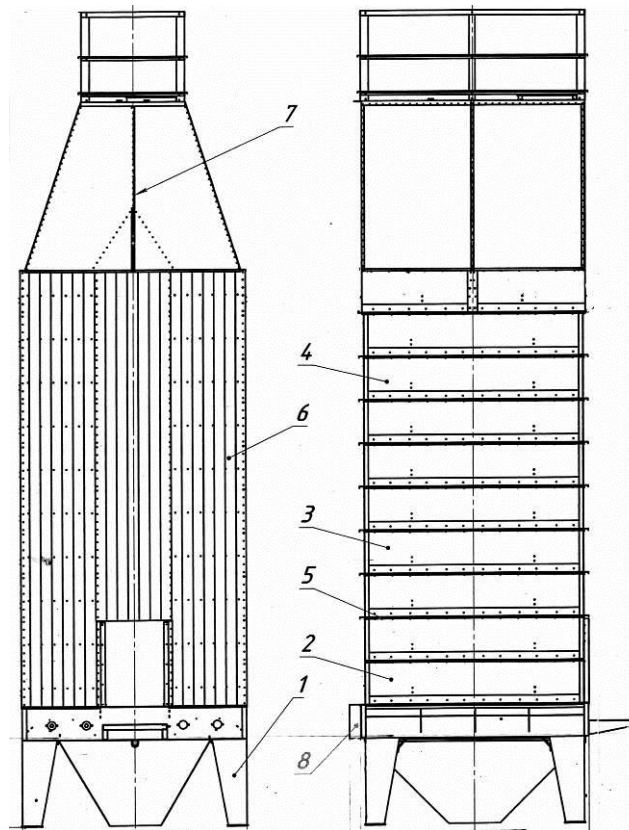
Загальний вигляд зерносушарки типу ЗШ в комплексі ЗАВ
